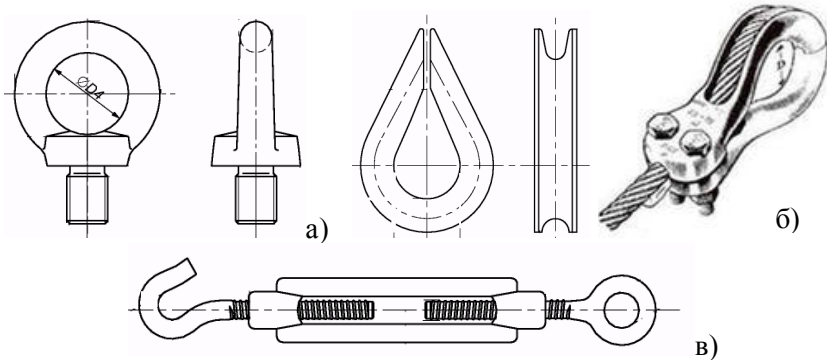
Такелажні пристосування: а – рим-болт; б – коуши; в – талреп
